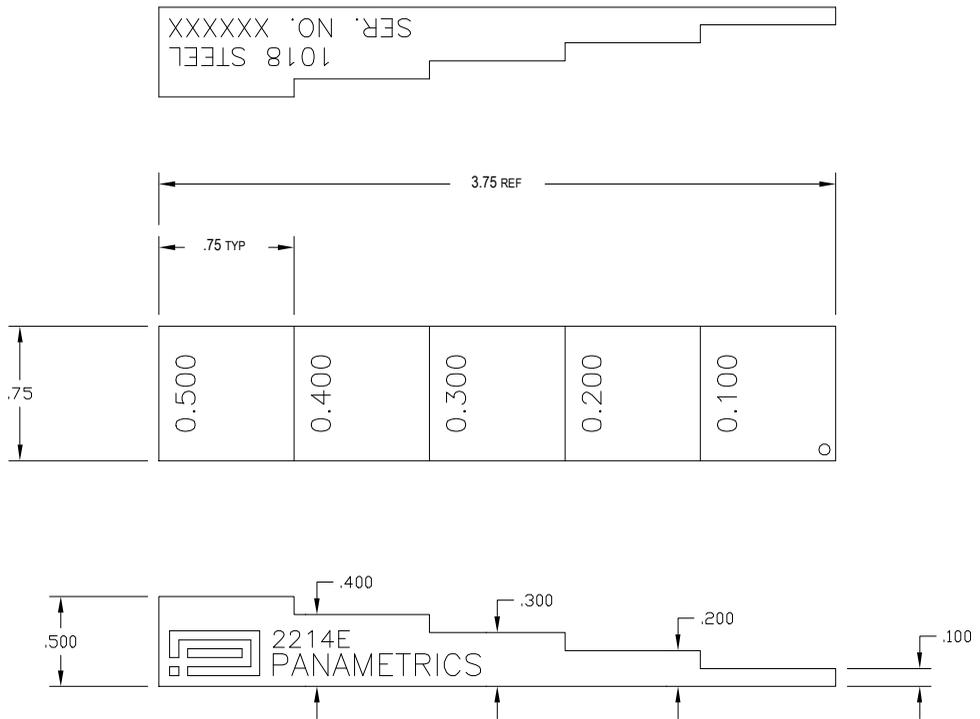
Пятиступенчатый калибровочный образец (Арт.: 2214E)
